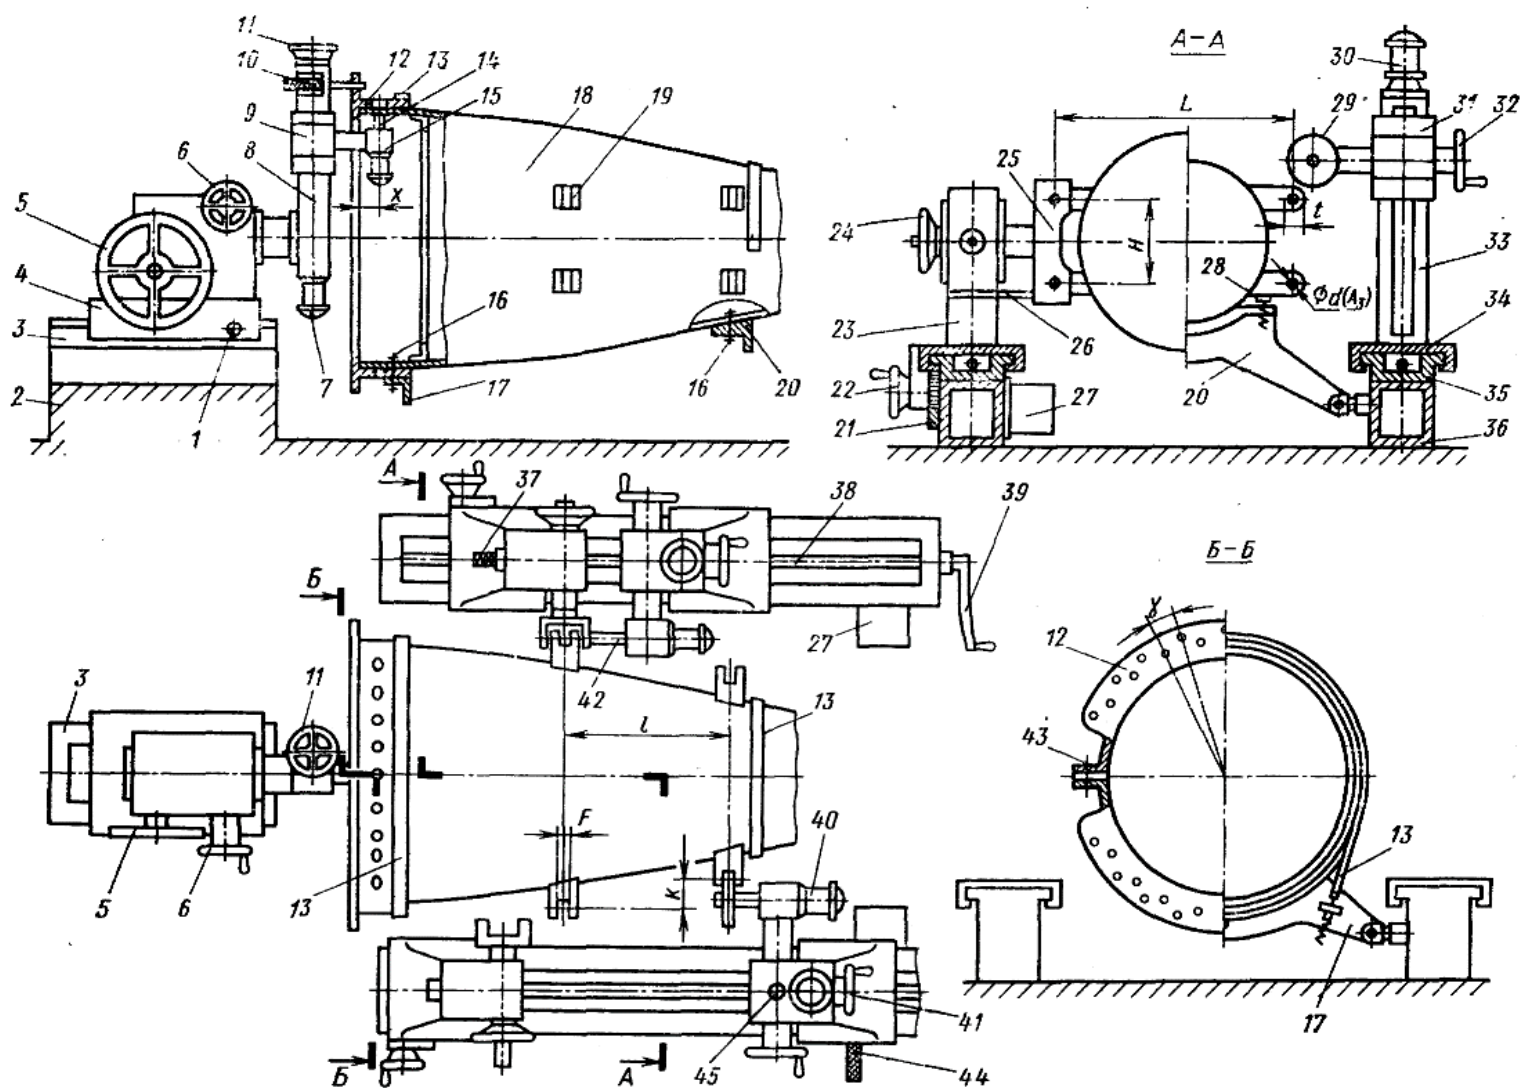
Разделочный стенд для обработки отверстий под заклепки (болты) технологического стыка и узлов крепления гондол двигателей на фюзеляже:
